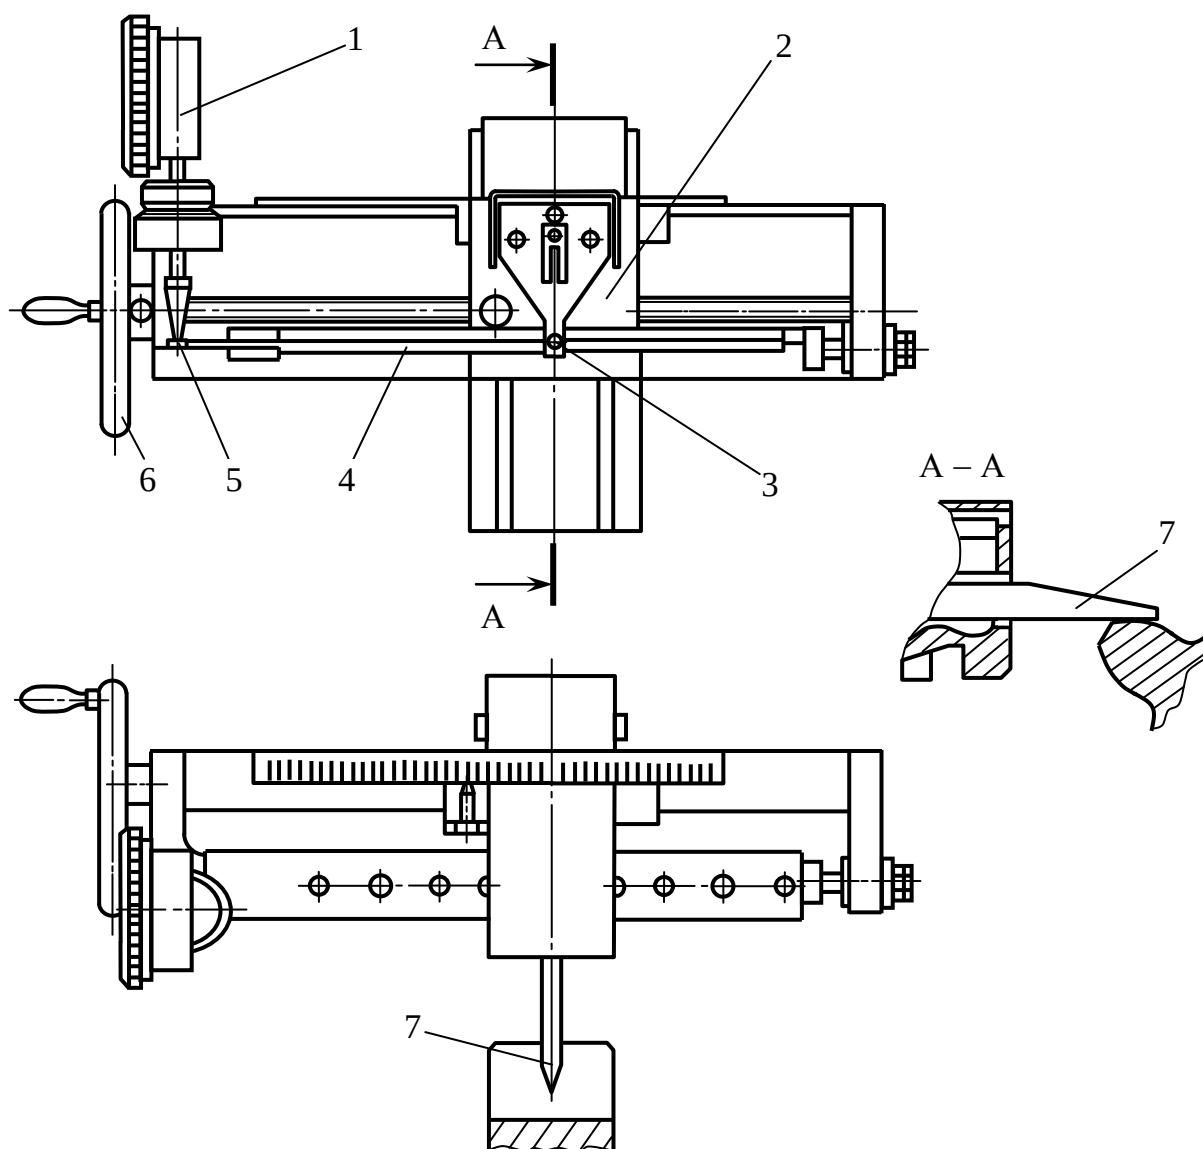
Наладка к прибору УЗП-400 для измерения отклонения направления зуба: 1 – измерительный прибор (индикатор часового типа); 2 – каретка; 3 – толкатель; 4 – рычаг; 5 – упор; 6 – маховичок; 7 – измерительный наконечник
